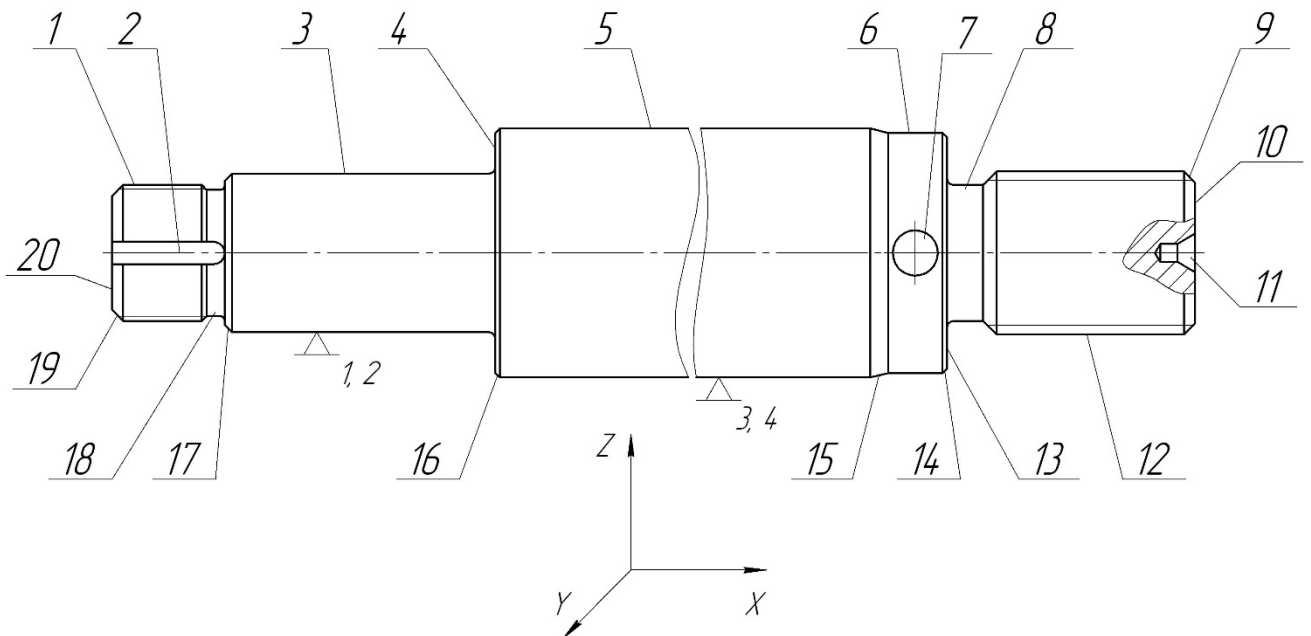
Схема базування штока в гідроциліндрі
